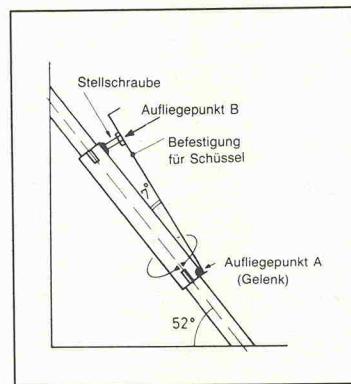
Selbstgebaute Polar-Mount-Befestigung nach Westra und Bruin.
